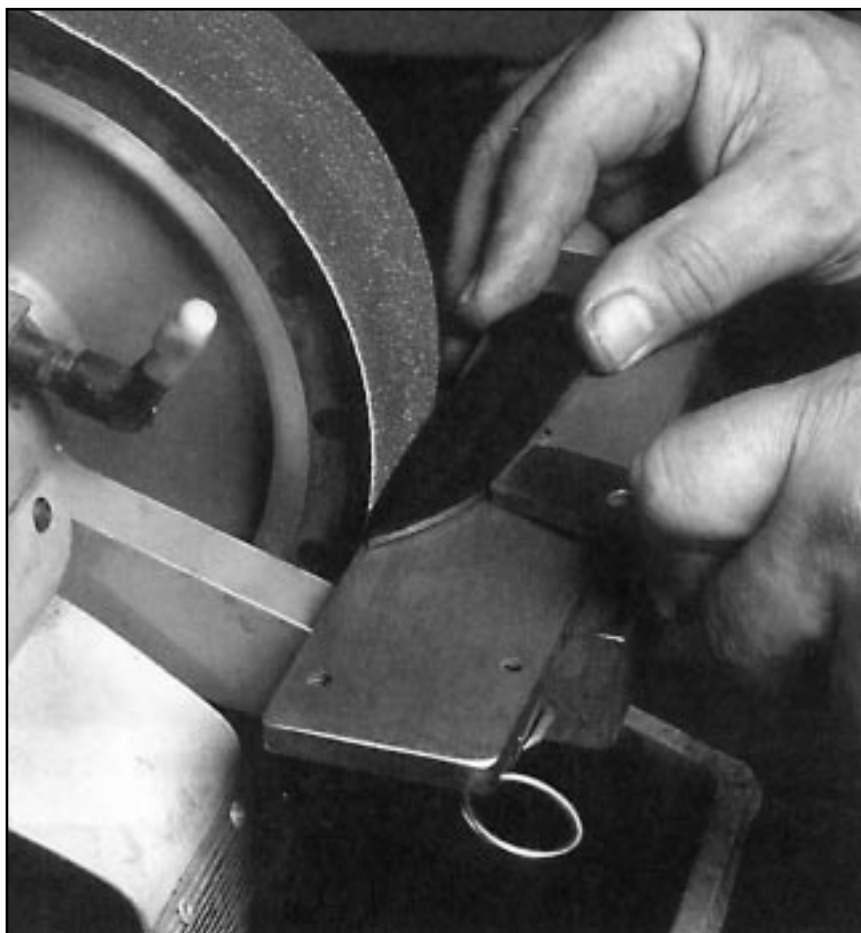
Отшлифуйте обрез заготовки клинка строго до очерченных линий.
